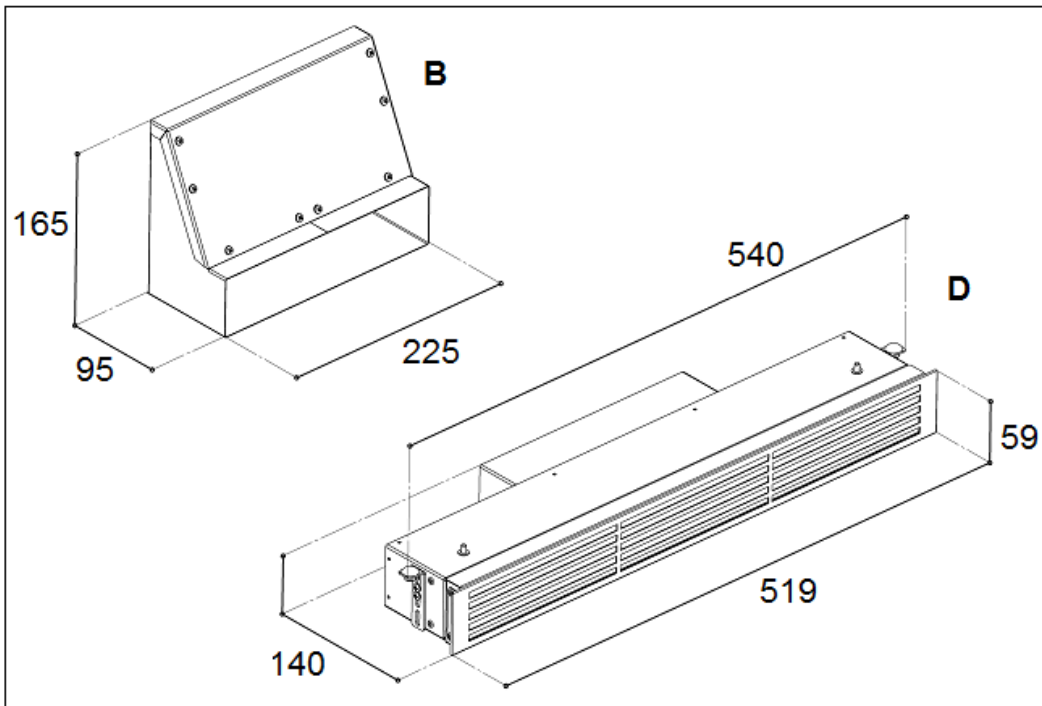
B e Fig. 5-D - Raccords, dimensions:
